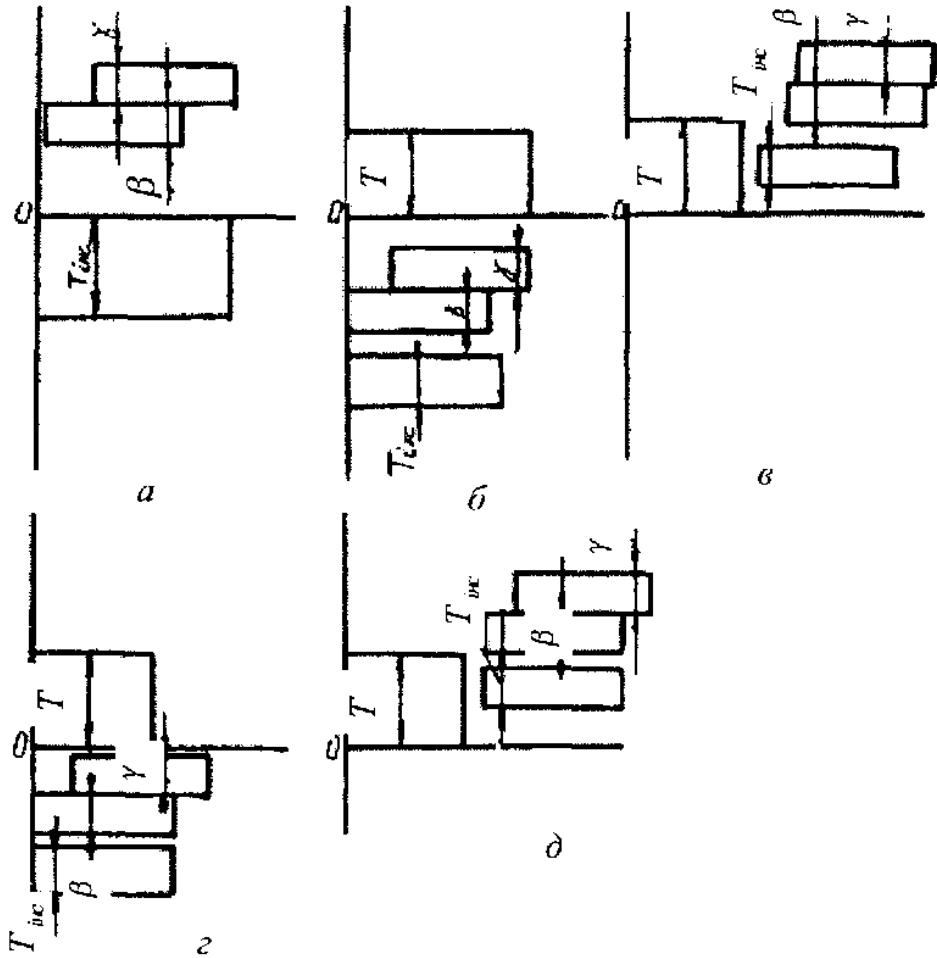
Схеми розташування полів допусків на діаметр отвору втулок: *a* – свердління; *б* – попереднє зенкерування; *в* – чистове зенкерування; *г* – попереднє розвертання; *д* – чистове розвертання
